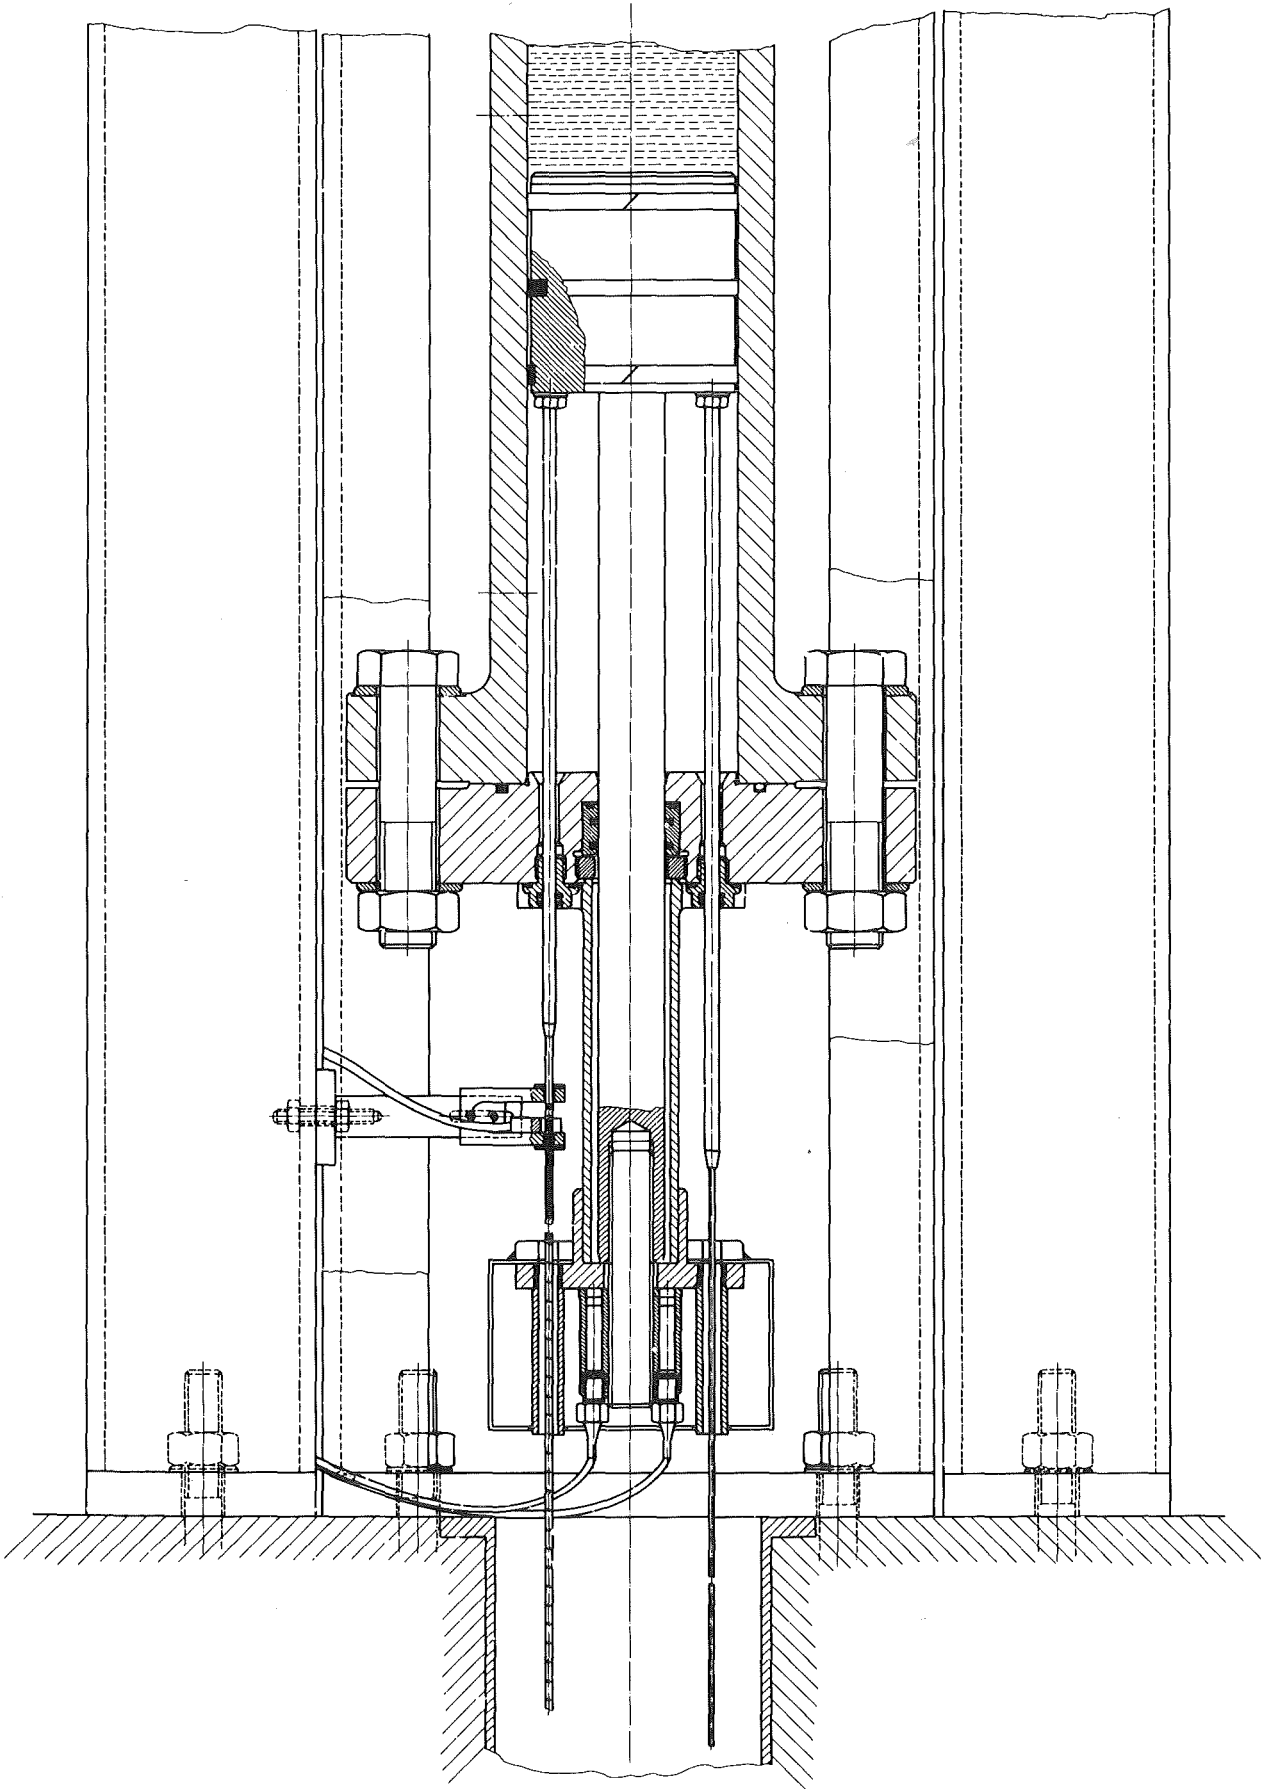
Beschleunigungsvorrichtung mit Explosionsmutter.
